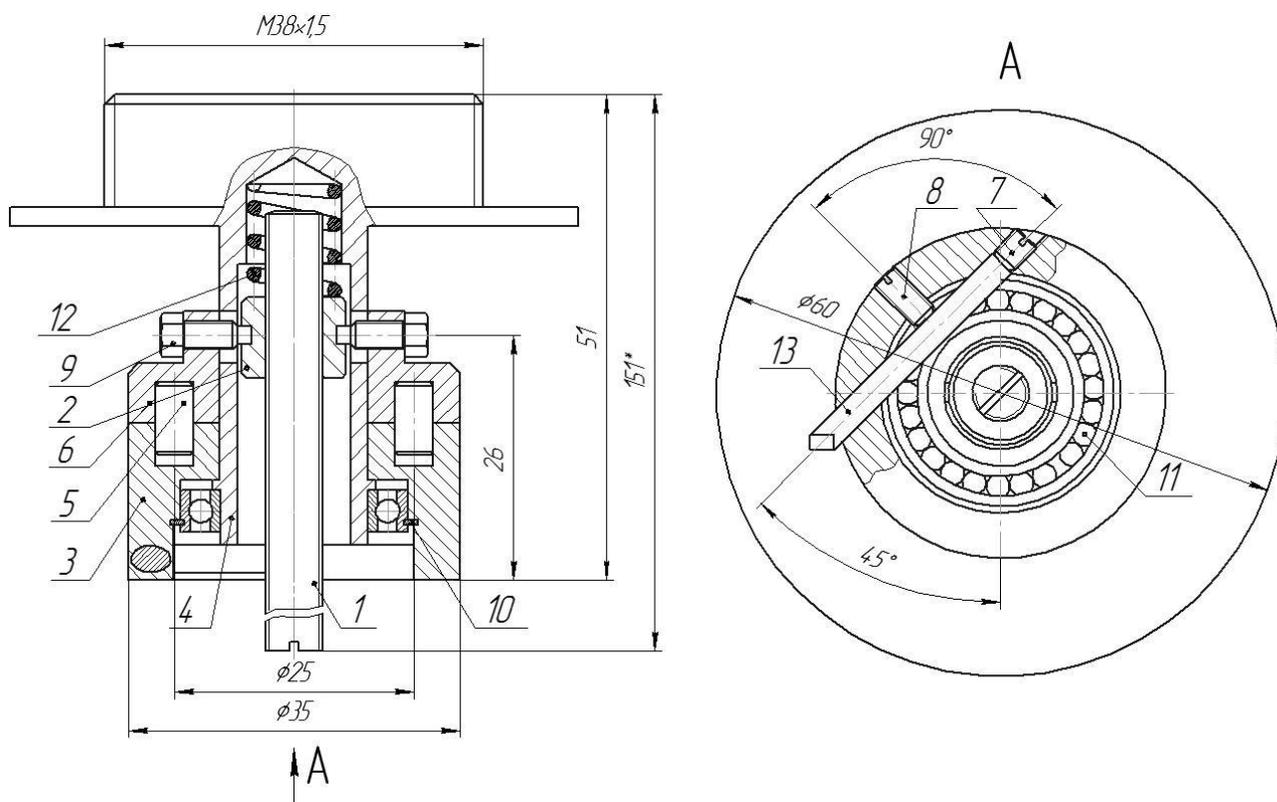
Приспособление для растачивания колодцев корпуса гидронасоса:
